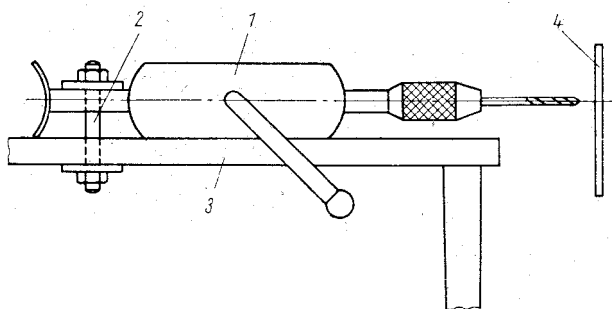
Zweckmäßigster Einsatz einer Handbohrmaschine (1) bei der Bearbeitung von Leiterplatten (4). (2) Schraubzwinge, (3) Tisch
